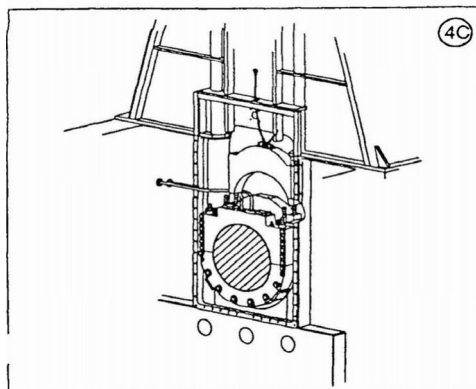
Демонтаж верхньої кришки підшипника
